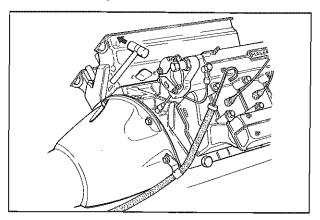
Smontaggio della testa cilindri Removing cylinder head
